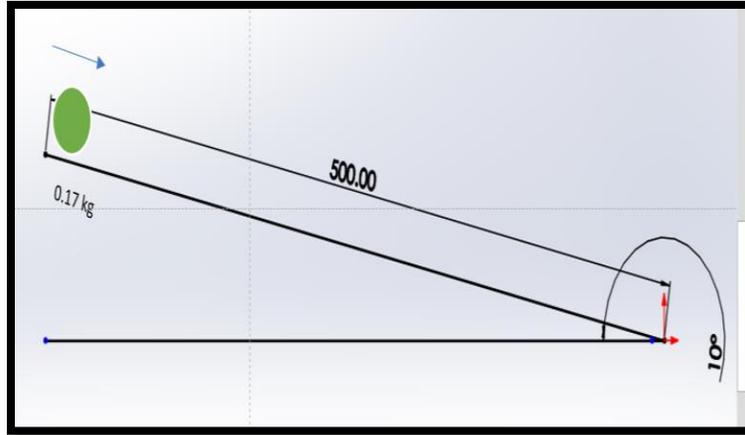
Representación del plano inclinado que forma la sección de dosificación.
